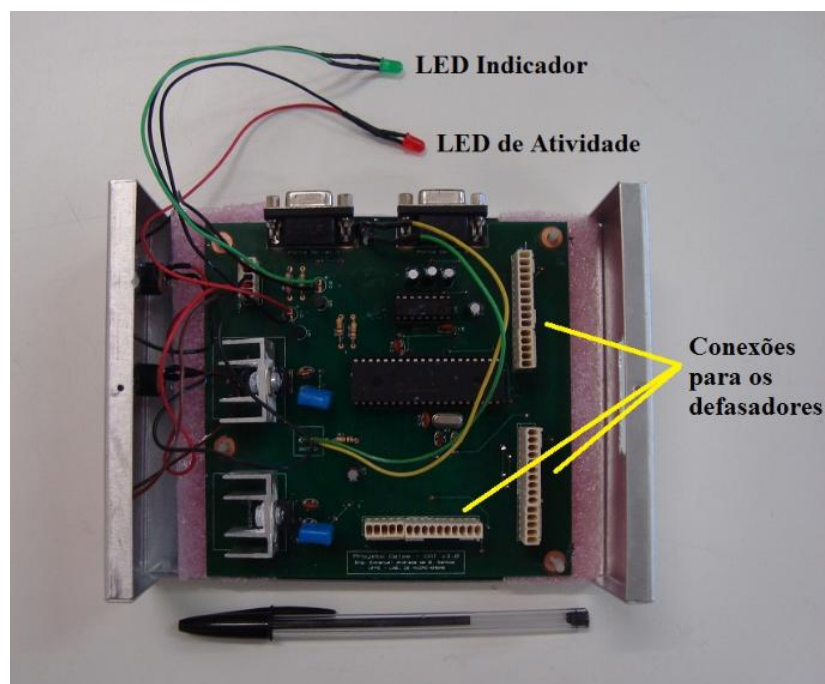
CAT versão 3 com componentes soldados.
